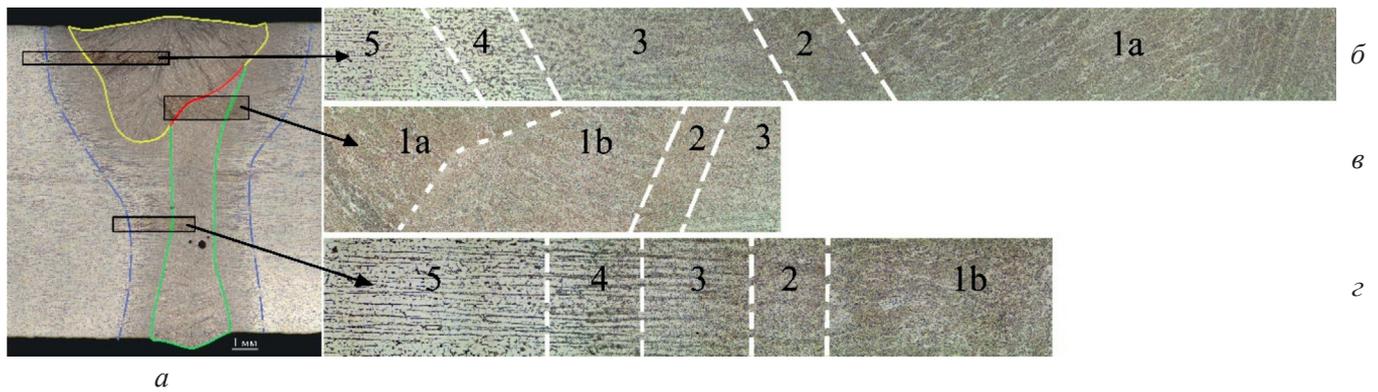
Микроструктура сварного соединения гибридной лазерно-дуговой сварки:
